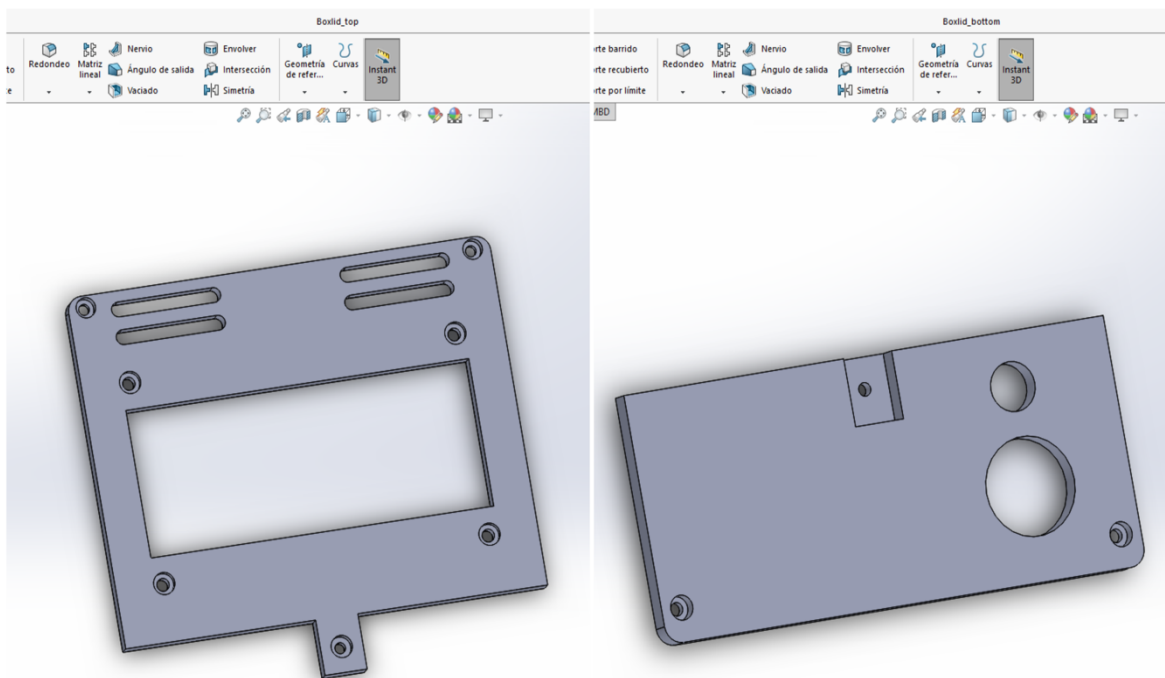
Diseño de la tapa frontal de la estructura de la caja. *Fuente: Autor.
